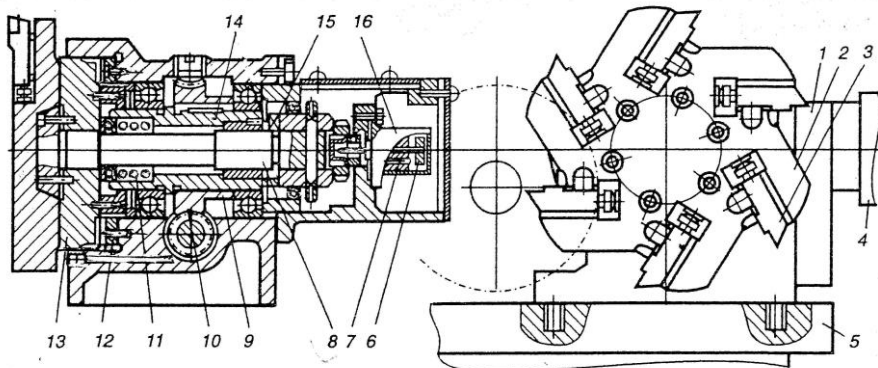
Шестипозиционная револьверная головка станка мод. 16К20Ф3С5
